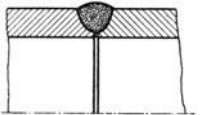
Tulpenförmige Schweißnaht.
